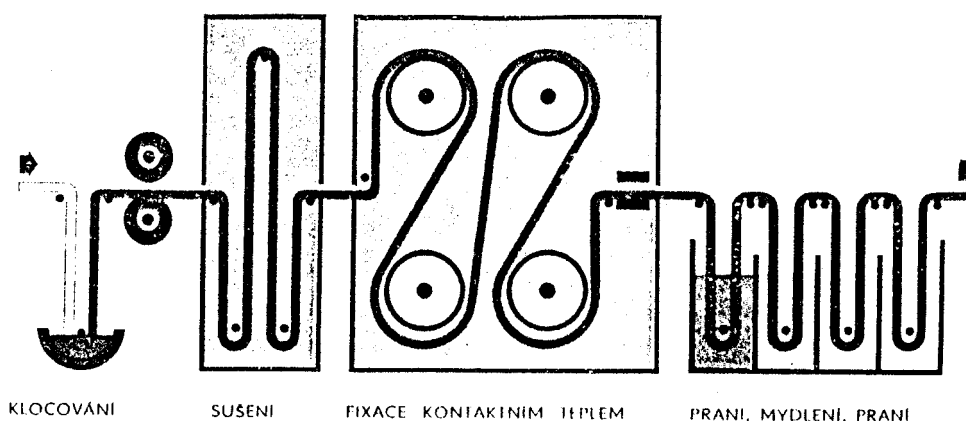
Schéma kontinuální technologie Pad - Dry
